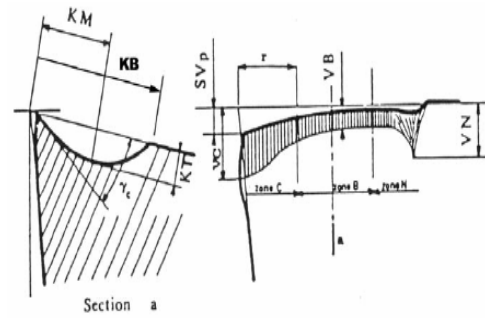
Mécanisme d'usure lié aux plaquettes carbures pour l'usinage de l'acier
